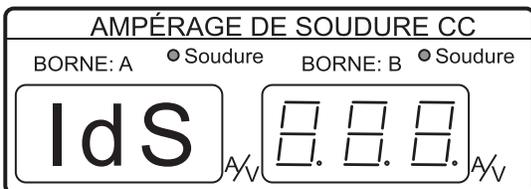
Mesureur de soudure à CC (arrêt au ralenti)
